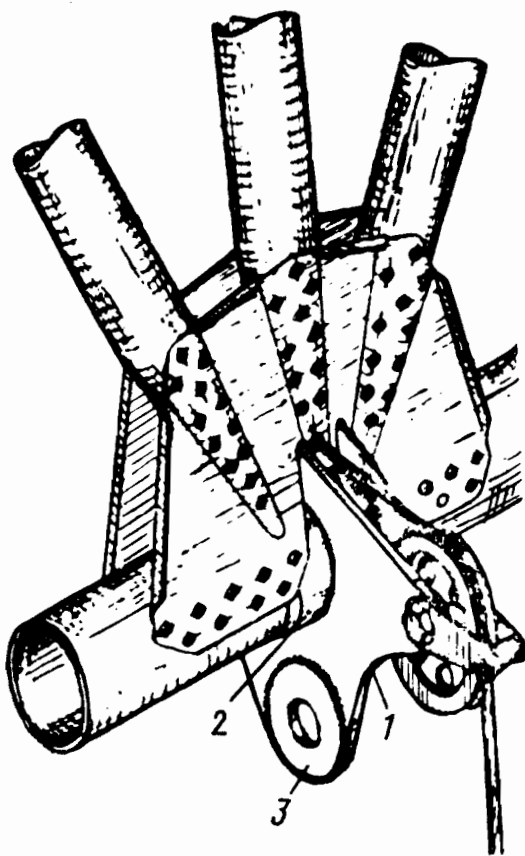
Узел крепления центроплана крыла к фюзеляжу (самолет АНТ-9)
